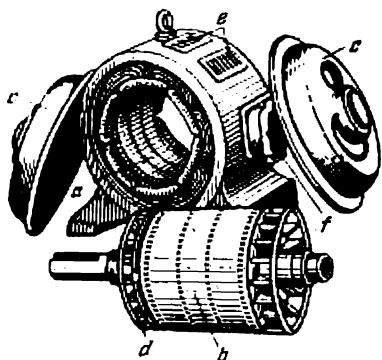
Moteur asynchrone à rotor en court-circuit démonté:
